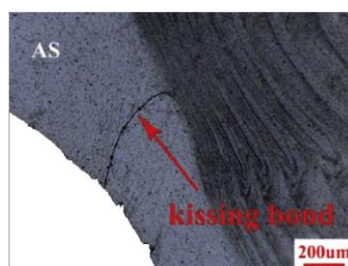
Figura 2.1 Defeito de falta de penetração (*kissing bond*) junto à concordância no lado de avanço [12].
